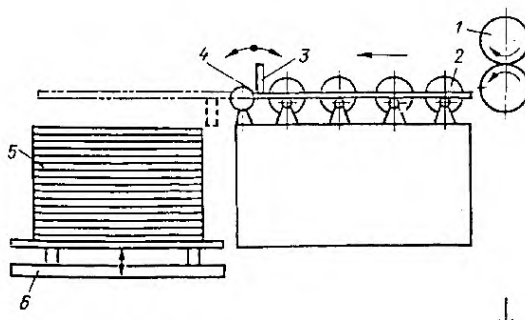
Устройство для механизации сборки пакетов шпона
